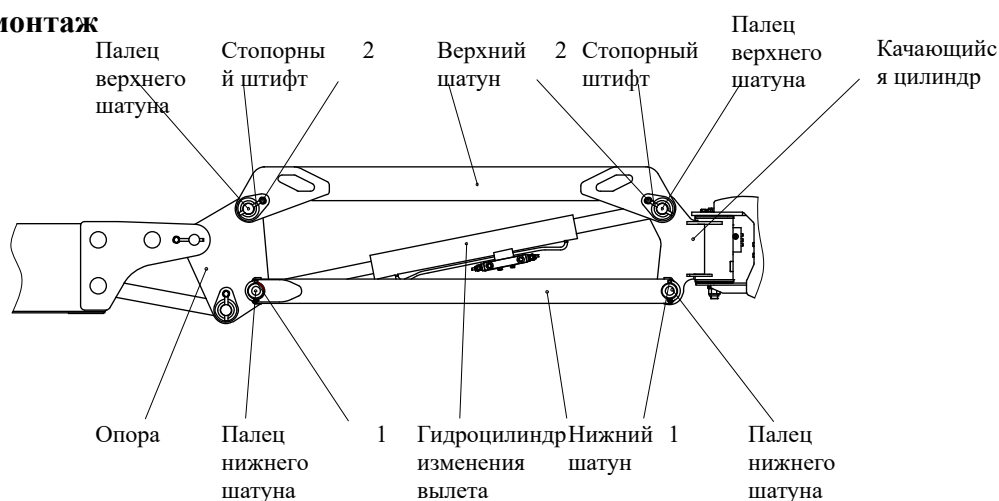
Схема демонтажа качающегося цилиндра, гидроцилиндра изменения вылета консоли
